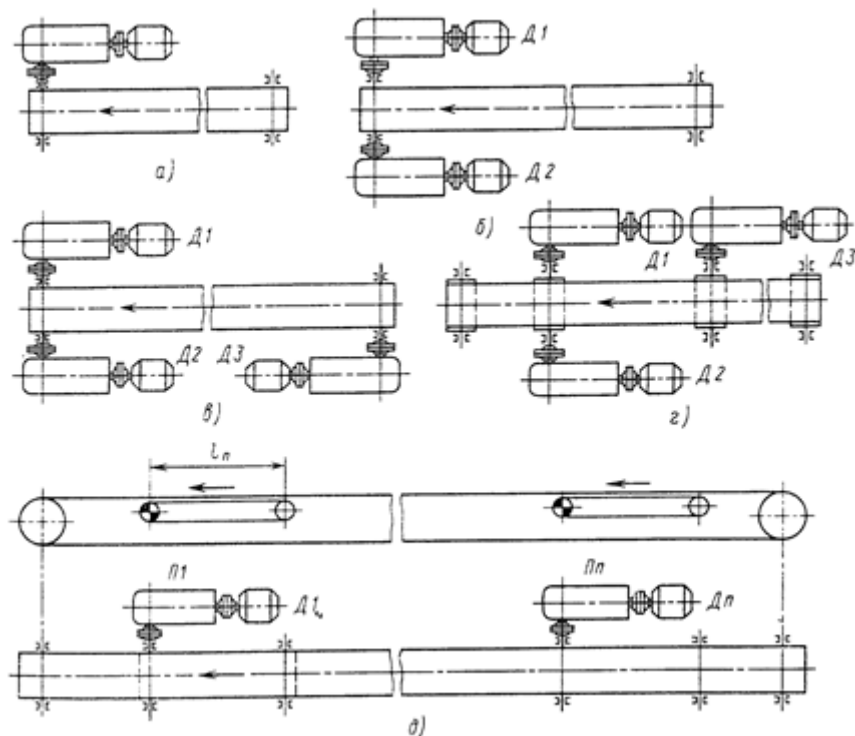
Схемы расположения приводов конвейеров: а – однодвигательного; б – двухдвигательного; в, г – трехдвигательного; д – многодвигательного с прямолинейными промежуточными приводами; П – привод; Д – двигатель
